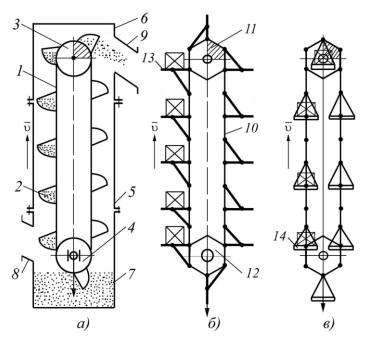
Элеваторы: а — ковшовый; б — полочный; в — люлечный; 1 — тяговый элемент в виде цепи или ленты; 2 — т грузонесущий элемент в виде ковша; 3 — приводной барабан; 4 — натяжной барабан; 5 — кожух; 6 — головка; 7 — башмак; 8 — загрузочный патрубок; 9 — разгрузочный патрубок; 10 — цепь; 11 — приводная звездочка; 12 — натяжная звездочка; 13 — грузонесущий элемент в виде полки: 14 — люлька
